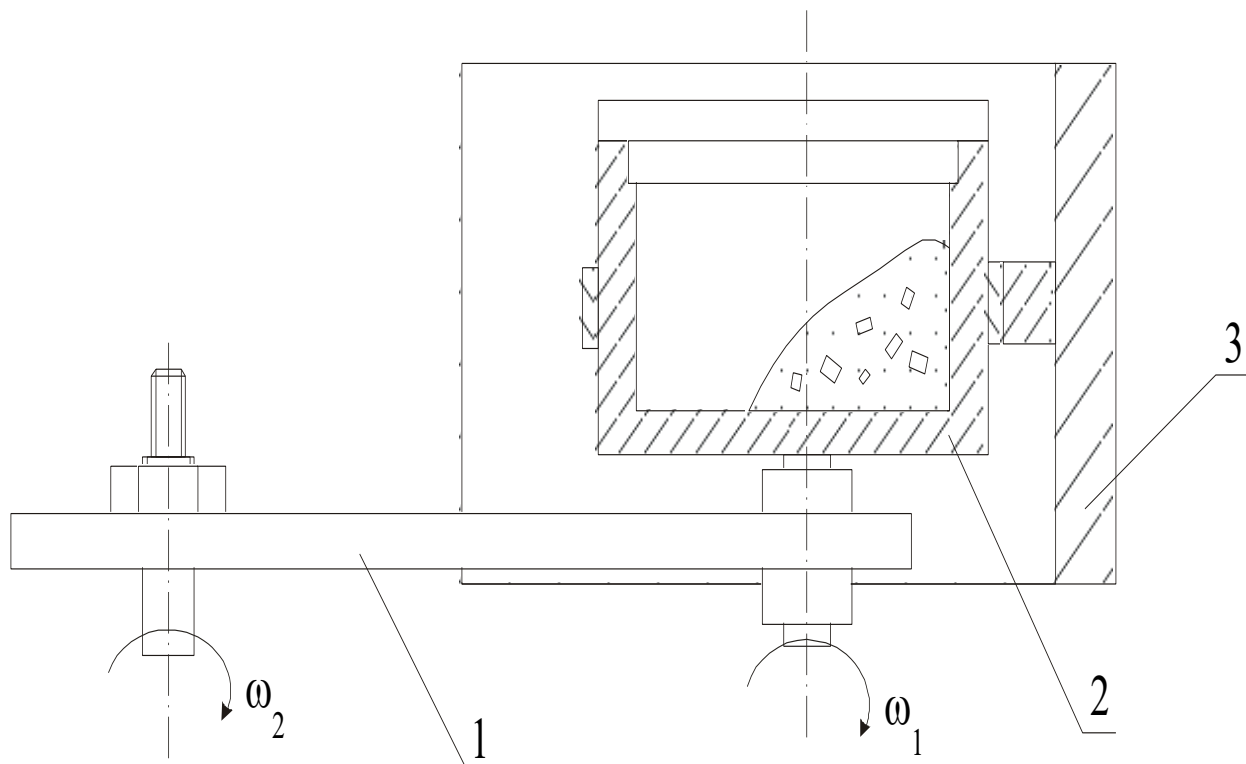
Схема обработки на планетарно-центробежном устройстве
